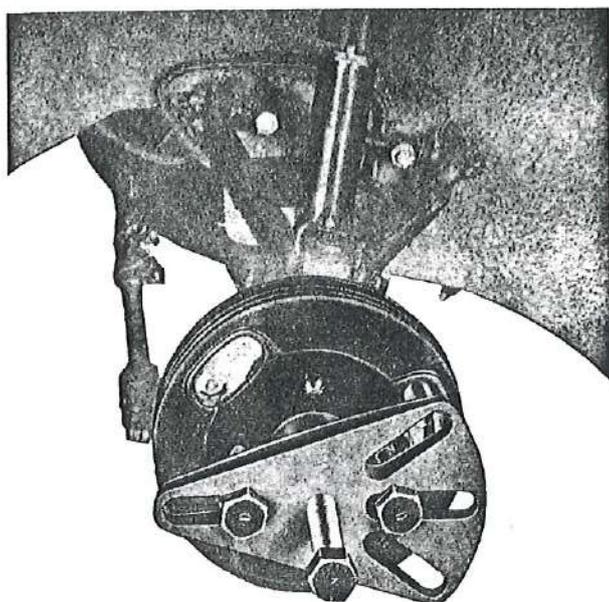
Extracción del tambor de freno de la rueda anterior izquierda, mediante el extractor A. 6469.
